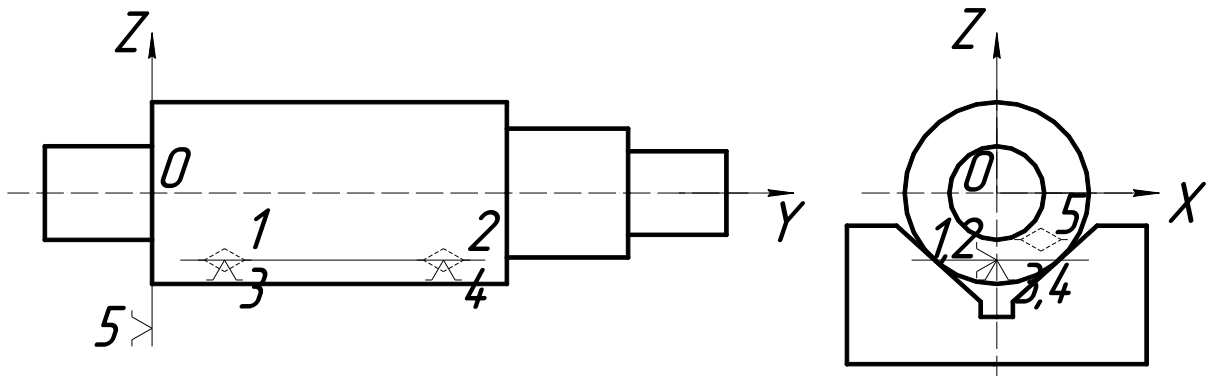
Базування за довгою зовнішньою поверхнею обертання
